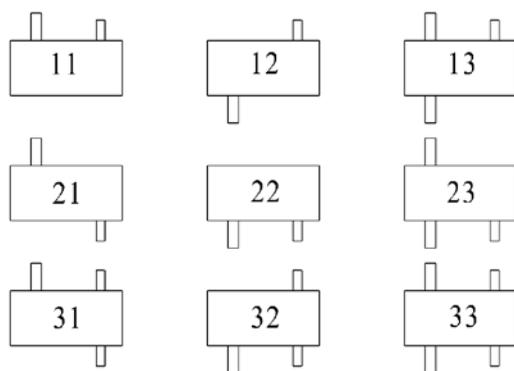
Варианты сборки цилиндрических редукторов 1Ц2У
